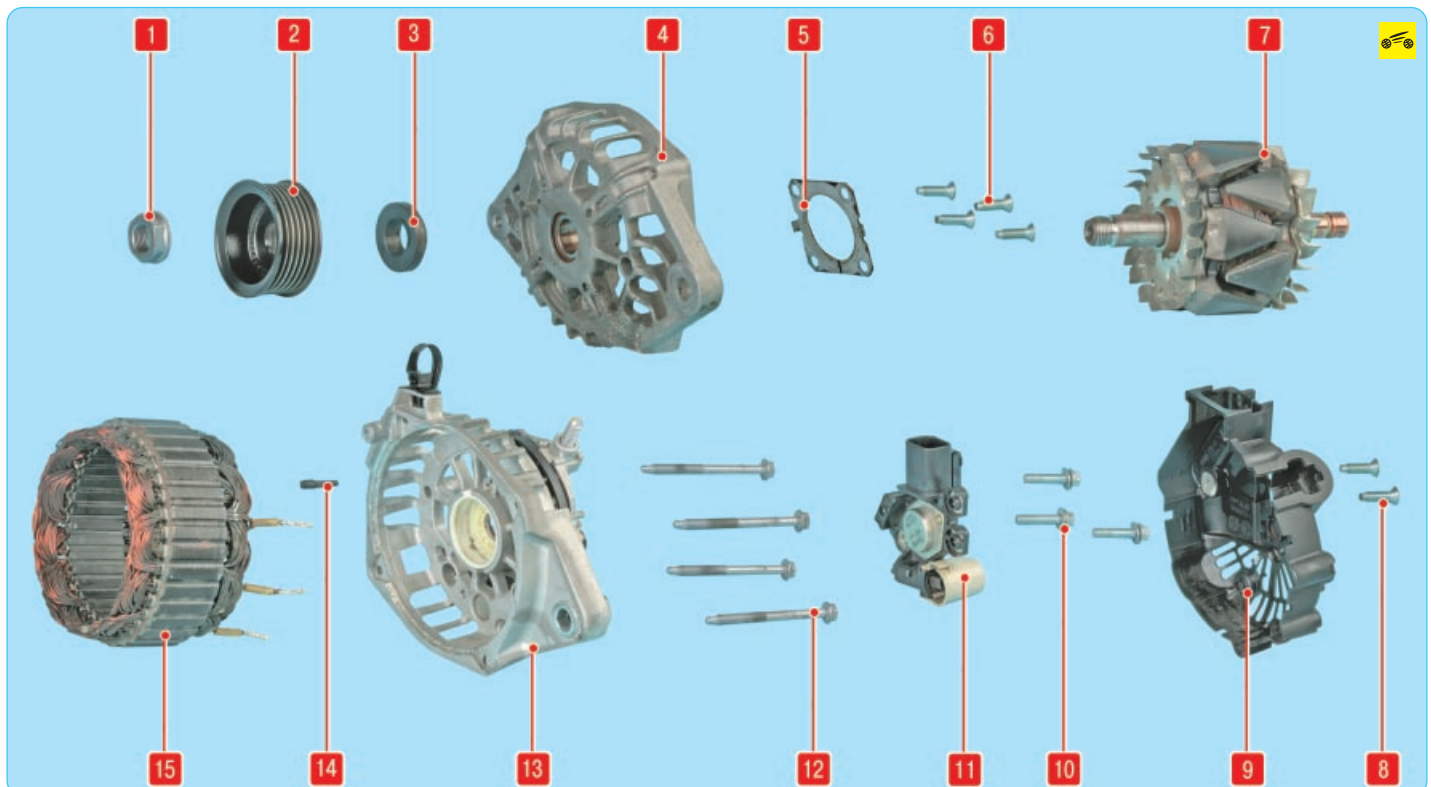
Детали генератора: 1 – гайка крепления шкива; 2 – шкив; 3 – дистанционное кольцо; 4 – передняя крышка; 5 – прижимная пластина подшипника; 6 – винт крепления прижимной пластины; 7 – ротор; 8 – винт крепления кожуха; 9 – кожух; 10 – болт крепления щеткодержателя; 11 – щеткодержатель с регулятором напряжения; 12 – стяжной болт; 13 – задняя крышка с выпрямительным блоком; 14 – установочный штифт; 15 – статор
